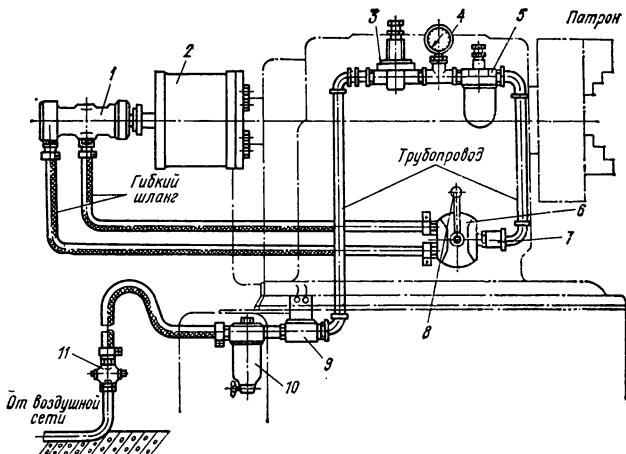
Монтажная схема пневмопривода к токарному станку
